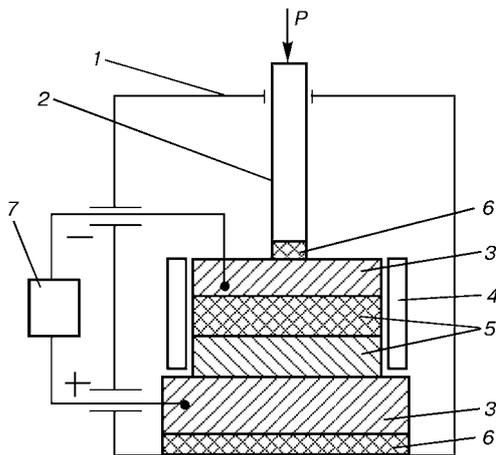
Принципиальная схема СЭП: 1 — вакуумная камера (при сварке в вакууме или в защитных газах) или электропечь (при сварке в воздухе); 2 — шток для передачи механического усилия (сварка без внешнего усилия сжатия); 3 — электроды; 4 — устройство для нагрева свариваемых деталей (радиационный нагрев); 5 — свариваемые детали; 6 — изоляторы; 7 — высоковольтный источник питания
